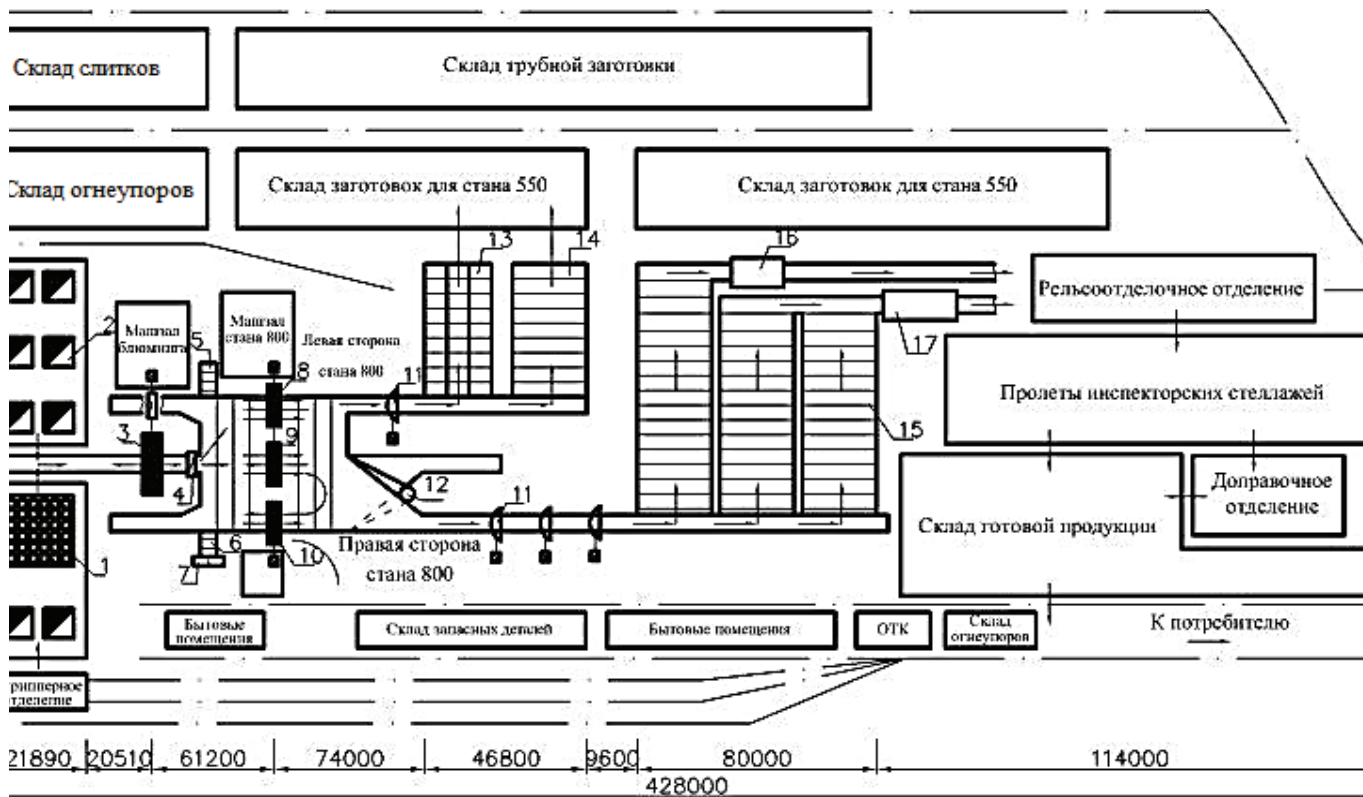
Схема размещения основного технологического оборудования прокатного цеха № 1: 1 – регенеративные нагревательные колодцы; 2 – рекуперативные нагревательные колодцы; 3 – рабочая клетка блюминга «1050»; 4 – парогидравлический нож; 5 – стеллажи для складирования заготовки; 6 – конвейер уборки технологической обрезки; 7 – яма для обрезки блюмсов; 8 – заготовочная клетка рельсобалочного стана «800»; 9 – черновая клетка стана «800»; 10 – чистовая клетка стана «800»; 11 – пилы горячей резки; 12 – механический отбойник; 13 – трёхсекционный холодильник; 14 – односекционный холодильник; 15 – трёхсекционный холодильник; 16, 17 – роликотправильные машины
